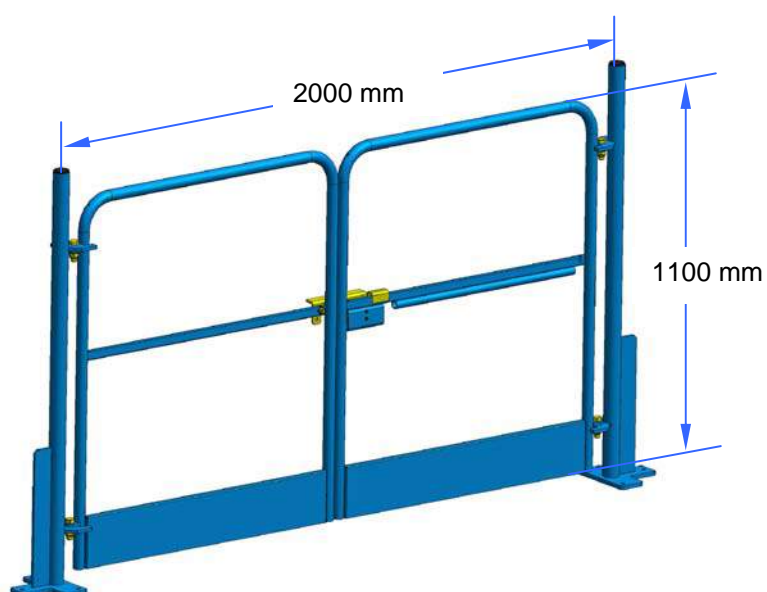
Dimensiones Puertas Seguridad en Planta (Altura reducida)
